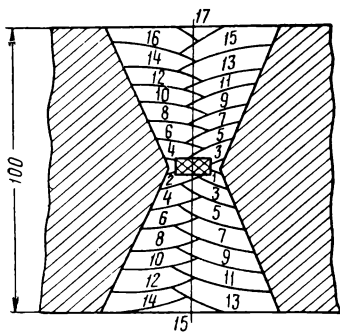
Порядок наложения сварочных швов при заварке трещин с Х-образной разделкой
